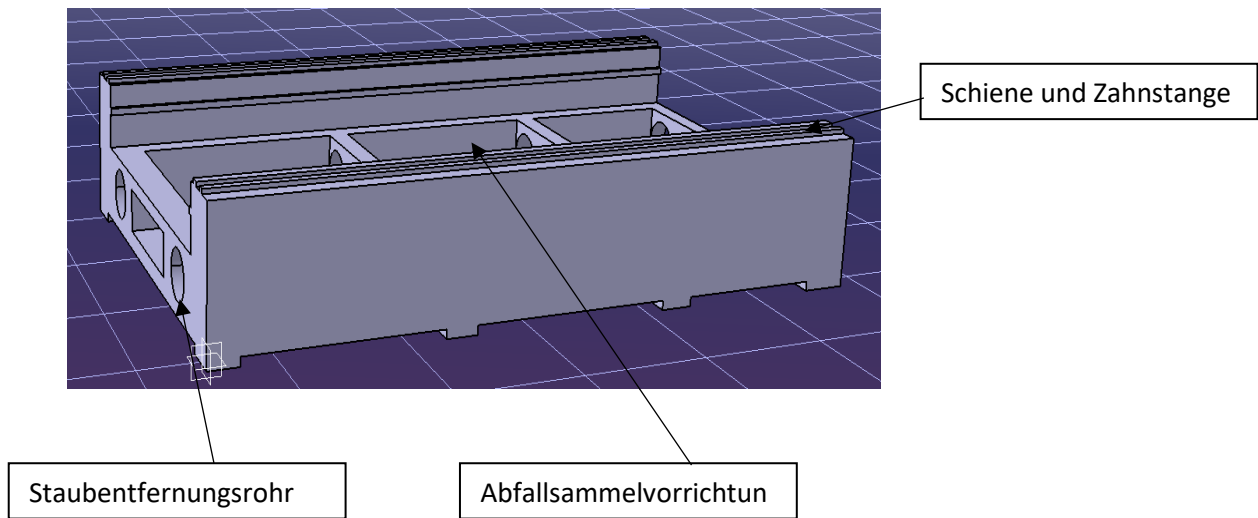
Aufbau der Werkzeugmaschinenbasis
